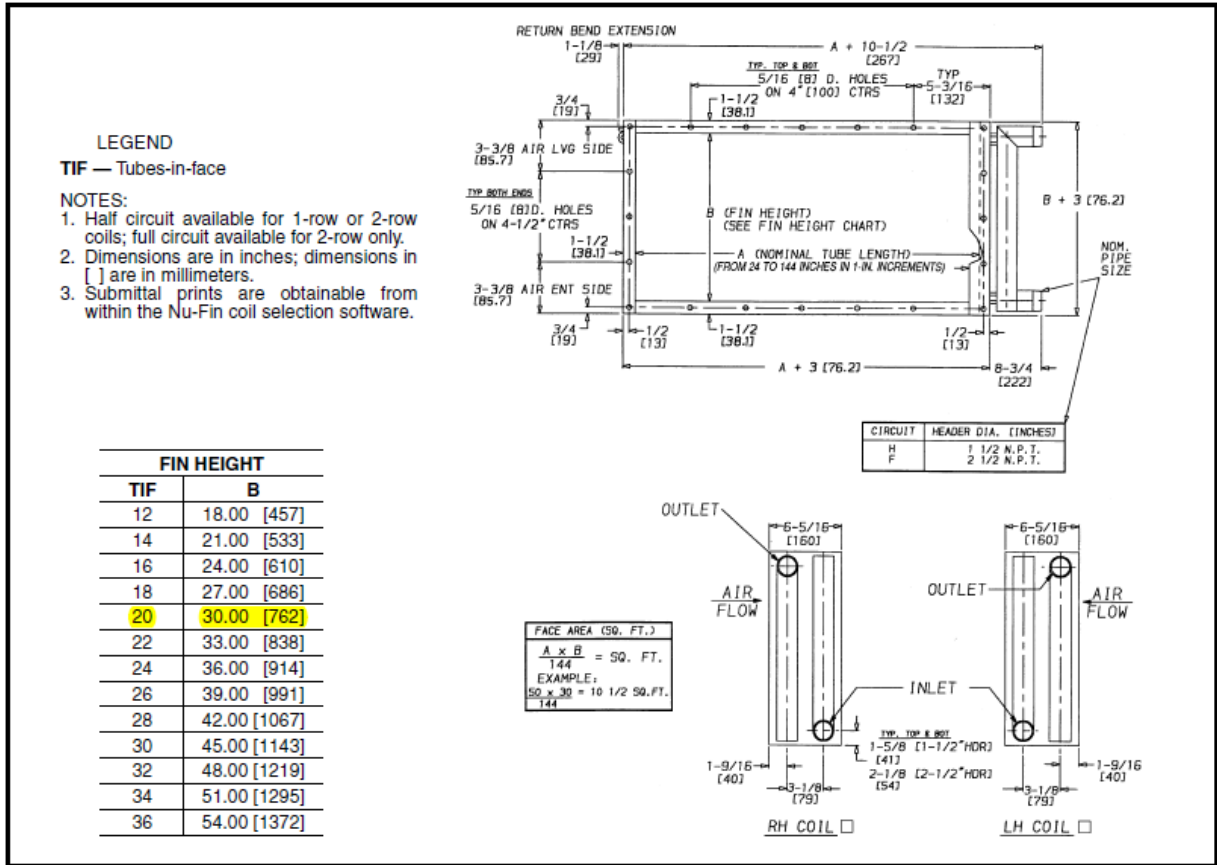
Dimensiones del serpentín de calentamiento UMA-01
